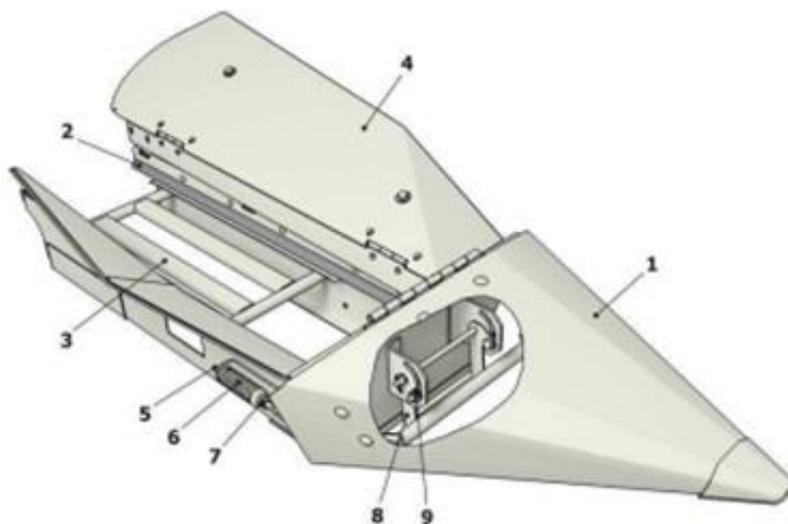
Лифтер: 1-делитель; 2-отлив; 3-каркас; 4-щиток; 5-тяги регулировочная; 6-пружина 7-гайка регулировочная; 8-упор; 9-болтокрепёж.
